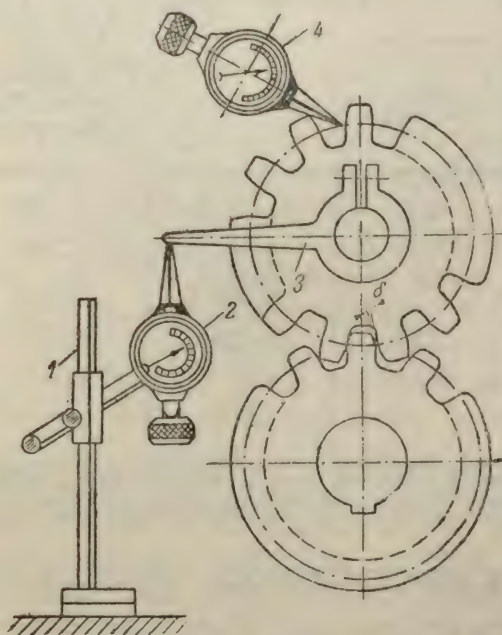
Проверка бокового зазора в зубчатой передаче при помощи поводка.
